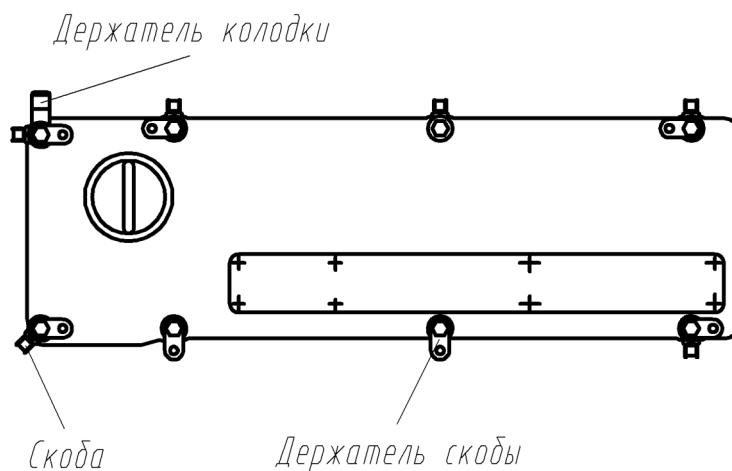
Схема установки скоб и держателей скоб крепления проводов
